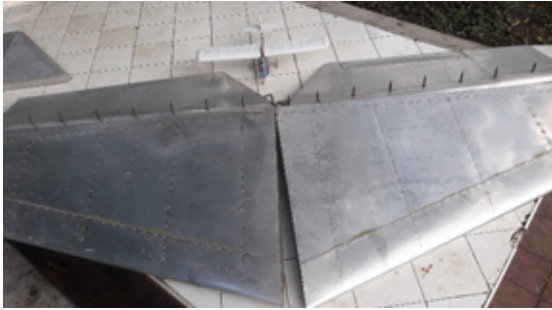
Estabilizadores horizontales de cola en proceso de manufactura. Fuente: El autor.
